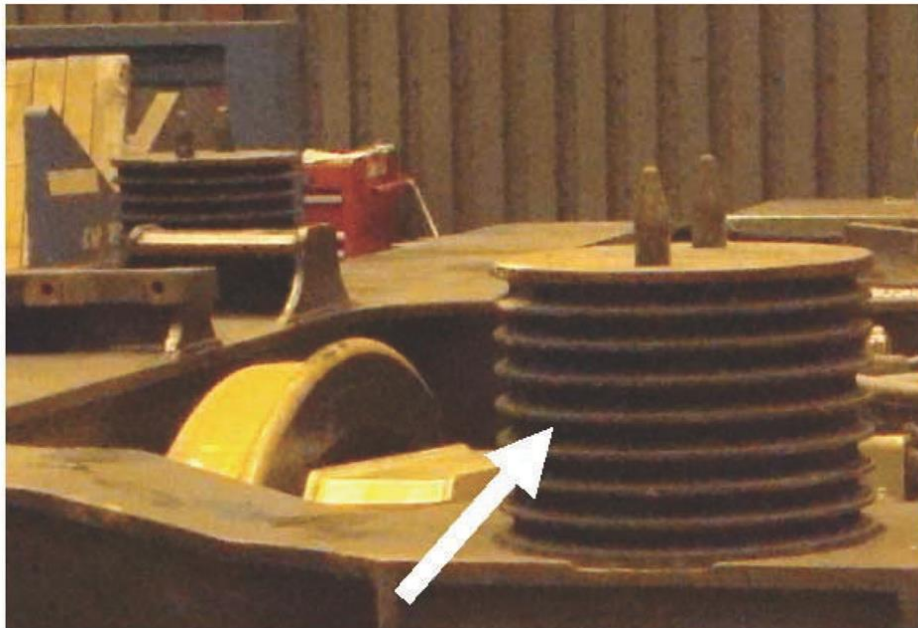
Бокова опора другої ступені ресорного підвішування
